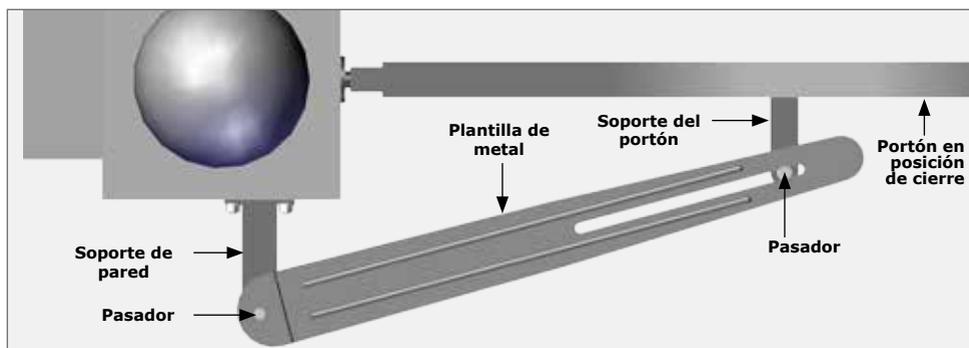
PORTÓN CERRADO (PLANTILLA DE METAL MONTADA)
